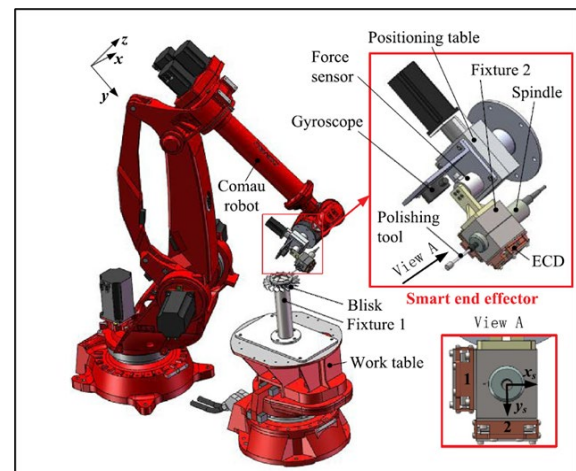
Установка для финишной обработки лопаток ГТД с умным выходным звеном [2]
